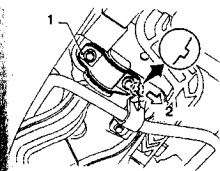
Положение установки зажима заднего шарнира рычага подвески (См. Раздел 5)
